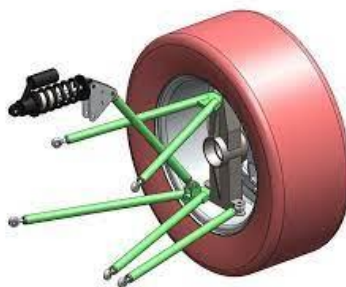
Exemple del dimensionat el 3D del sistema de suspensió Push-rod.
